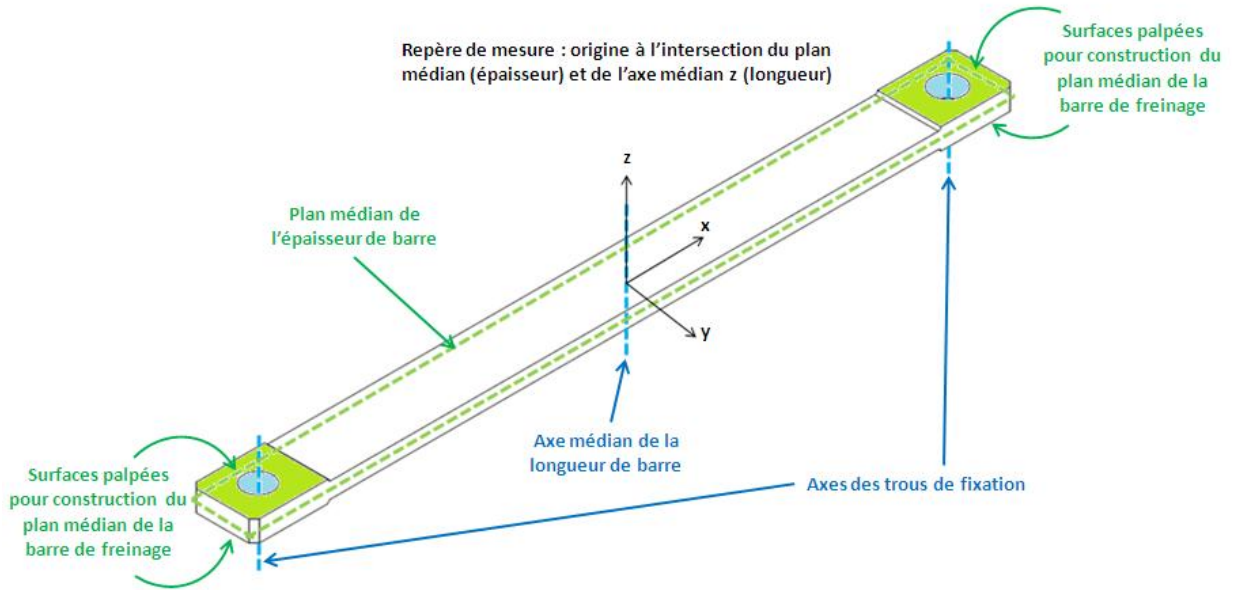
Construction du repère pour les mesures de profil de barre sur MMT.
